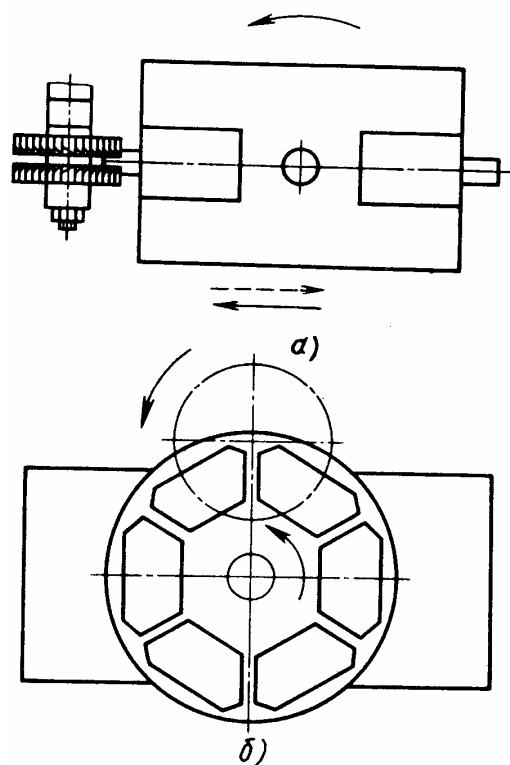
Схеми фрезерування заготовок: а – при закріпленні їх на поворотному столі в двох пристосуваннях; б – на вертикально-фрезерному верстаті з обертовим столом
